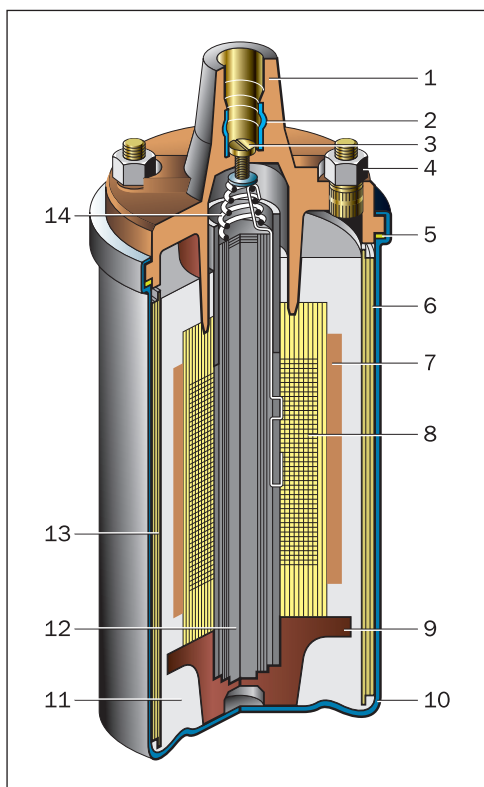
Конструкция катушки зажигания: 1 — крышка; 2 — контактное гнездо; 3 — винт; 4 — вывод низкого напряжения; 5 — уплотнительная прокладка; 6 — кольцевой магнитопровод; 7 — первичная обмотка; 8 — вторичная обмотка; 9 — фарфоровый изолятор; 10 — кожух катушки; 11 — трансформаторное масло; 12 — сердечник; 13 — картонная прокладка; 14 — контактная пружина
